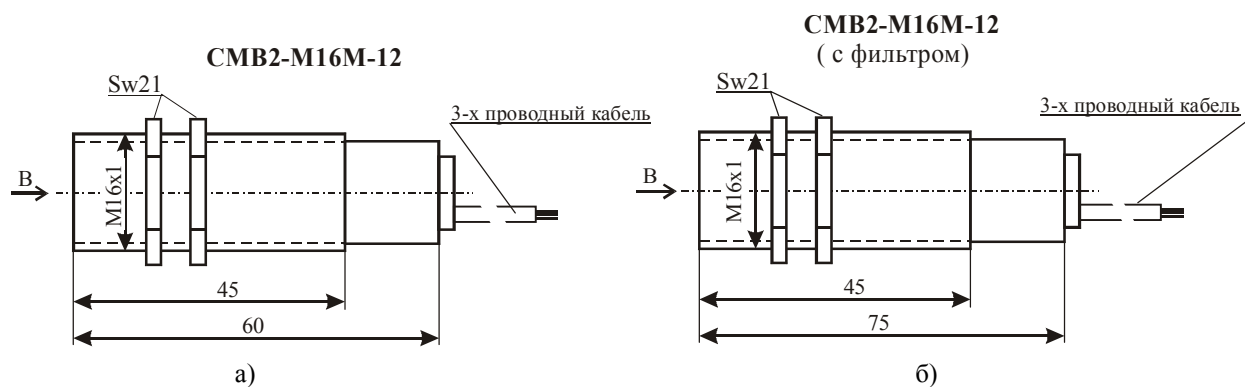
Внешний вид и габаритные размеры датчиков типа CMB2-M16M-12: а – без фильтра; б – с фильтром
